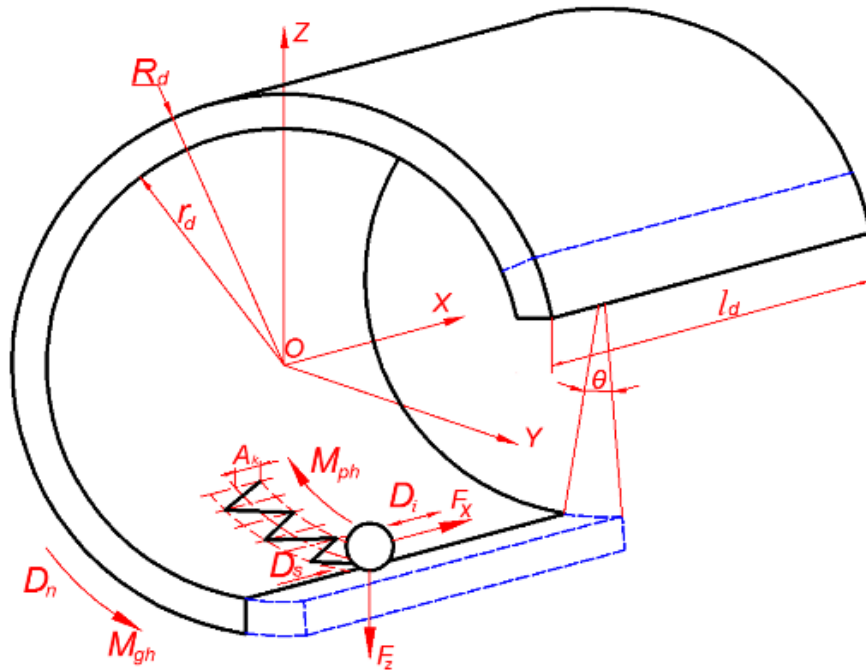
Схема формування регулярного мікрорельєфу на внутрішній циліндричній поверхні деталі
